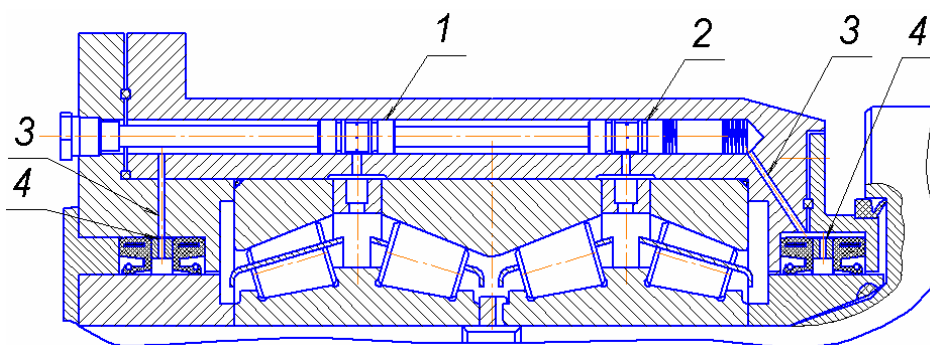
Установка делителей потока для смазывания подшипника и манжет
